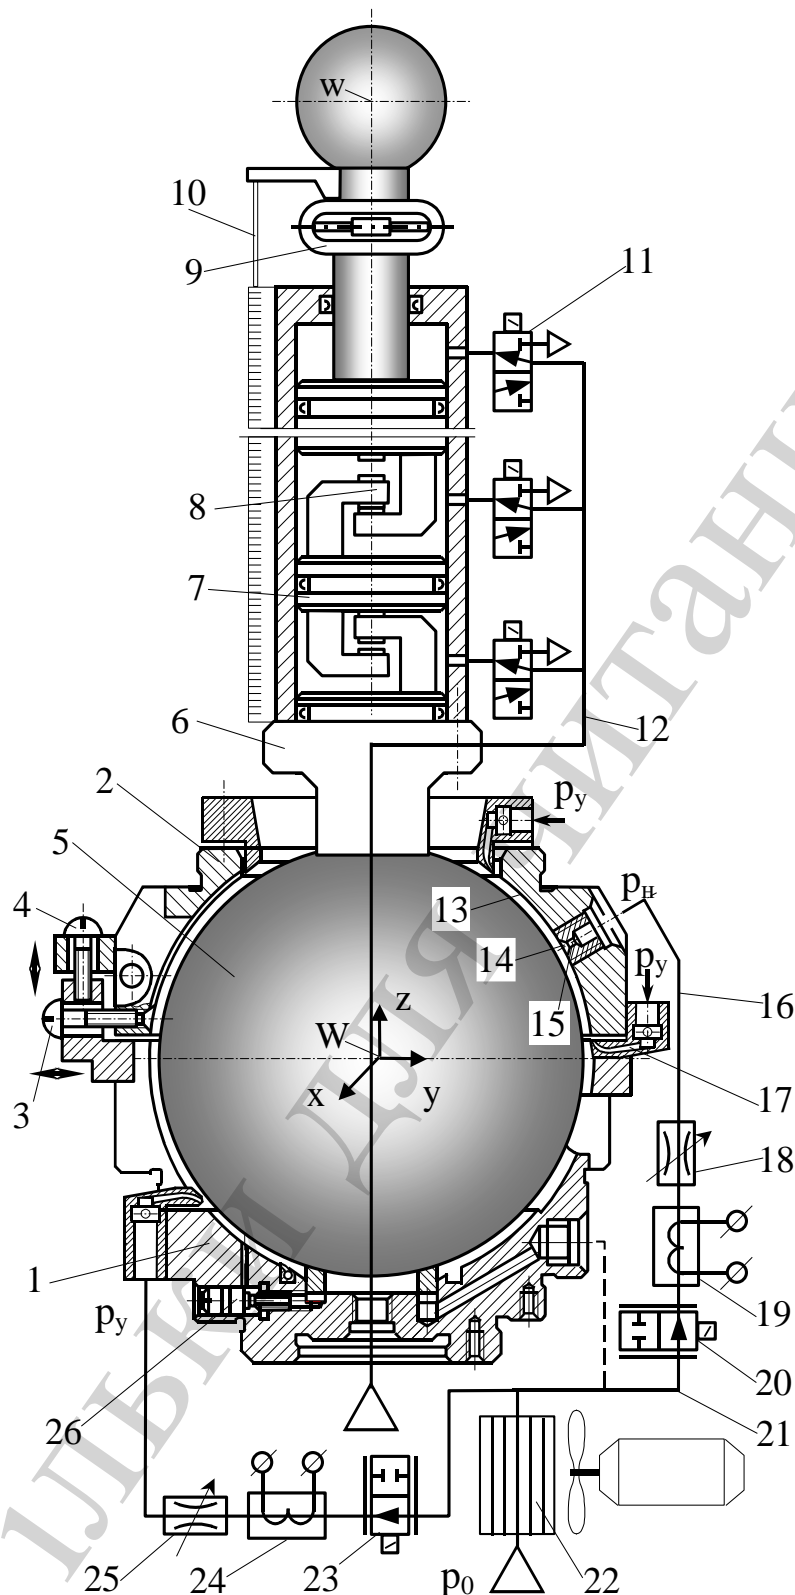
Конструктивна схема регульованої аеростатично-гідростатичної сферичної опори з приводом зміни довжини штанги: 1 – корпус; 2 – кришка; 3, 4 – гвинтові приводи; 5 – точна сферична поверхня; 6 – штанга маніпулятора; 7 – поршні; 8 – упори; 9 – пристрій мікропереміщень; 10 – вимірювач; 11 – регульовані дроселі; 12 – магістраль; 13 – кармани; 14 – дросель; 15 – опорні вузли; 16 – магістраль; 17 – сопловий пристрій; 18 – дросель; 19 – нагрівач; 20 – розподільник; 21 – магістраль; 22 – радіатор; 23 – розподільник; 24 – нагрівач; 25 – регульований дросель
